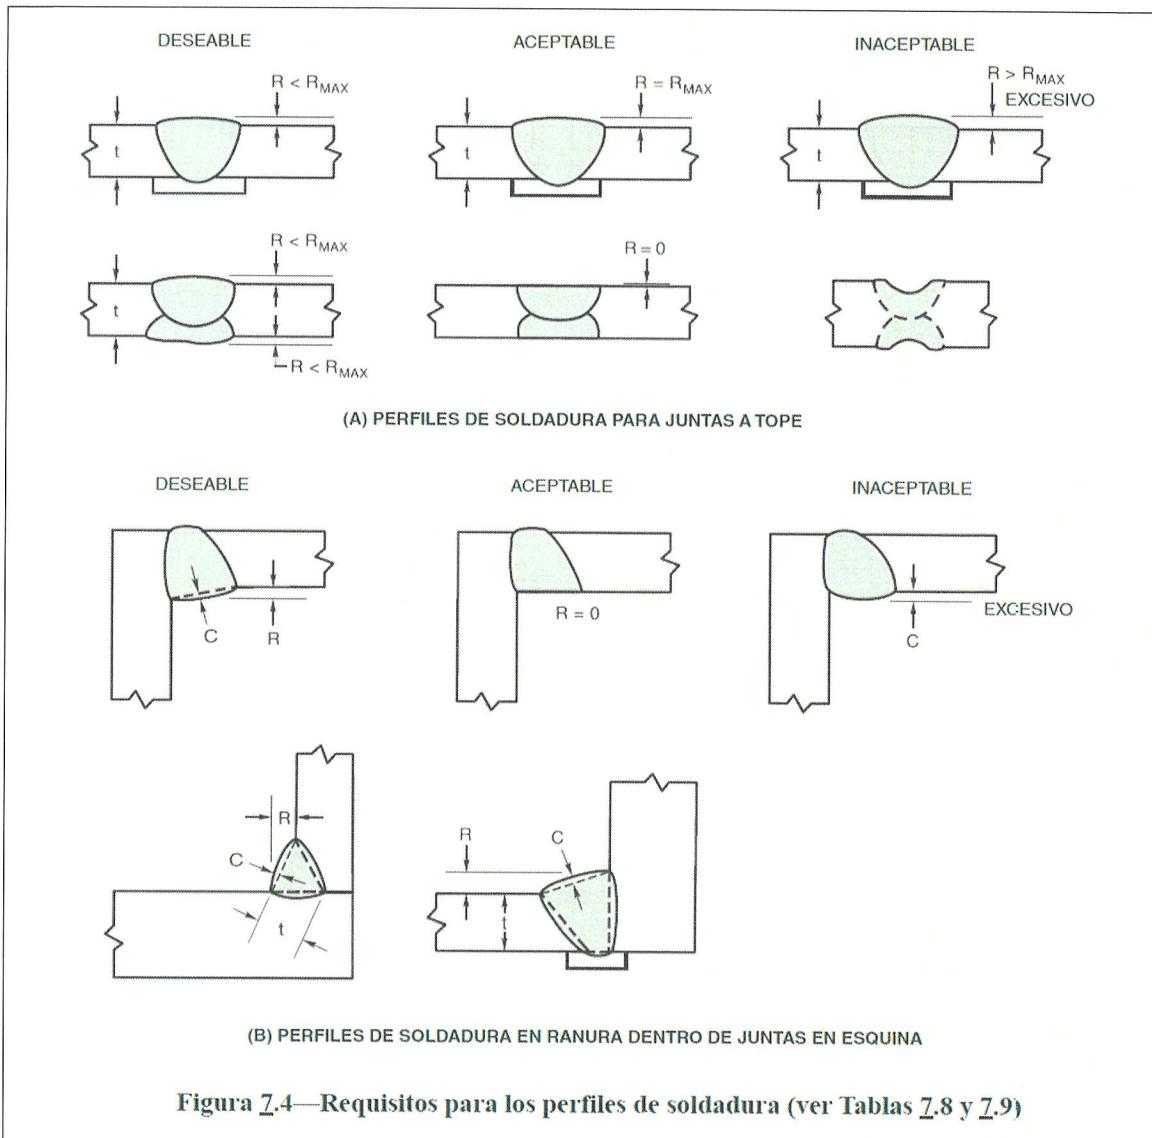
Requisitos para los perfiles de soldadura (ver Tablas 7.8 y 7.9)
